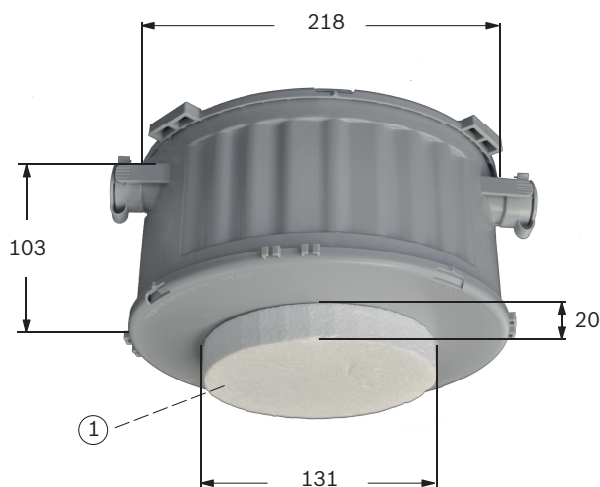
Встраиваемый корпус FAA-500-CB
